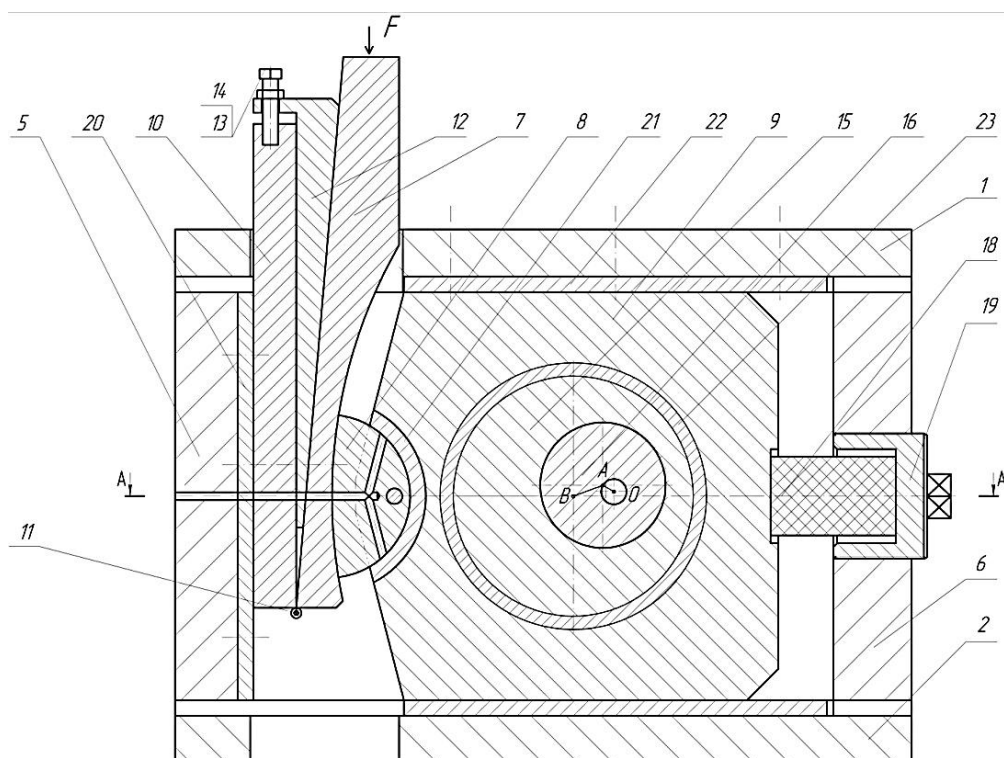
Установка для разделения труб эксцентричным закручиванием
